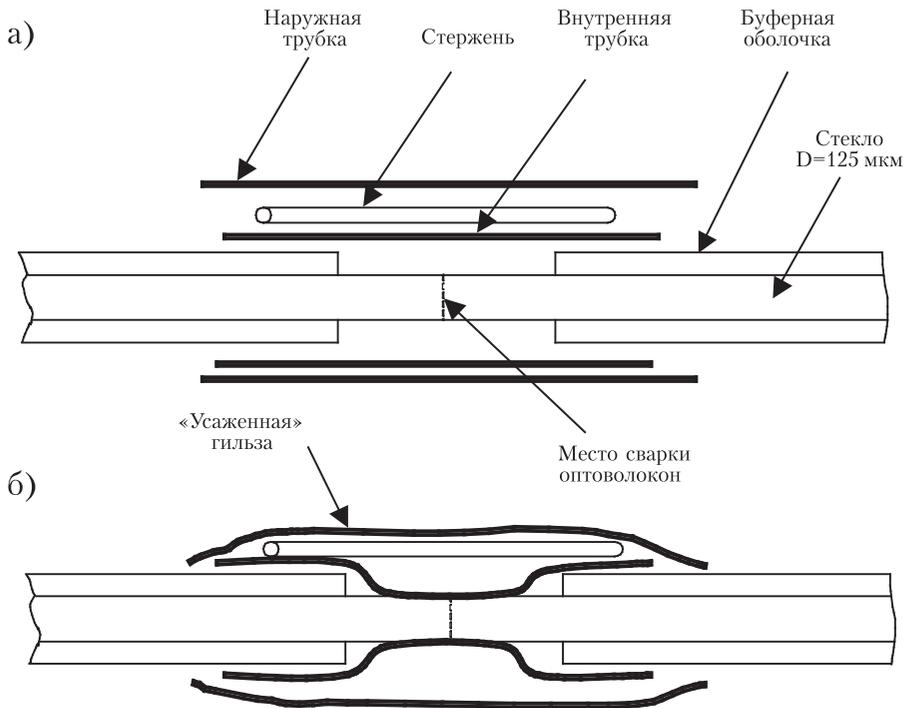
Схема сварного сплайса оптоволоконна:
